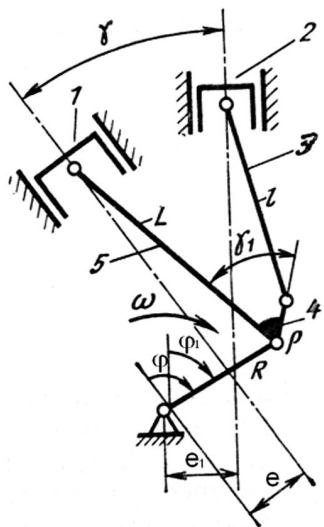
Кривошипно-шатунный механизм с прицепным шатуном: 1 – главный цилиндр; 2 – боковой цилиндр; 3 – прицепной шатун; 4 – прицеп; 5 – главный шатун; γ – угол развала цилиндров; γ_1 – угол отклонения прицепного шатуна; φ – текущее значение угла поворота кривошипа, отсчитываемого от оси главного цилиндра; φ_1 – текущее значение угла поворота кривошипа относительно оси цилиндра прицепного шатуна, r – расстояние от оси шатунной головки кривошипа до оси пальца прицепного шатуна
